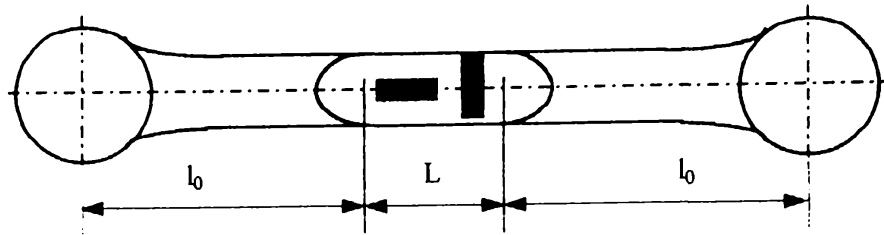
Delimitarea zonelor constructive pe o bară de măsurare
